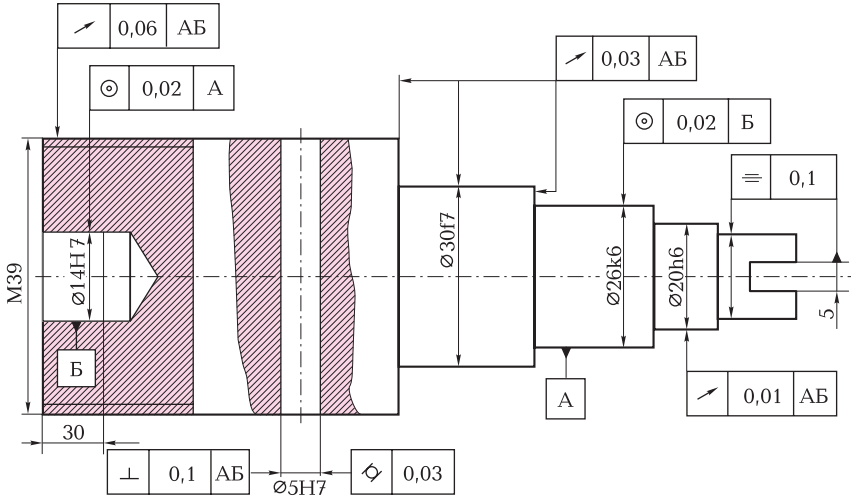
Условные обозначения допусков формы и расположения поверхностей на детали типа «вал»
